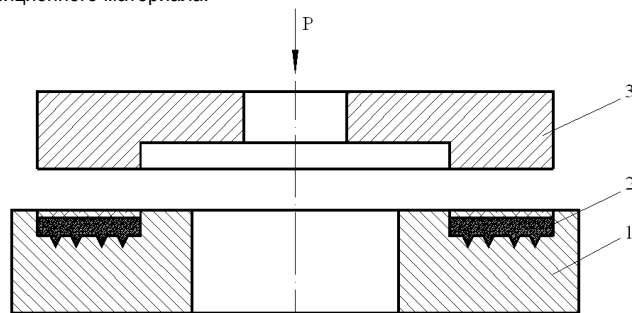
Схема прессовки шихты в кольцевом пазу заготовки: 1 – заготовка; 2 – шихта; 3 – пуансон
